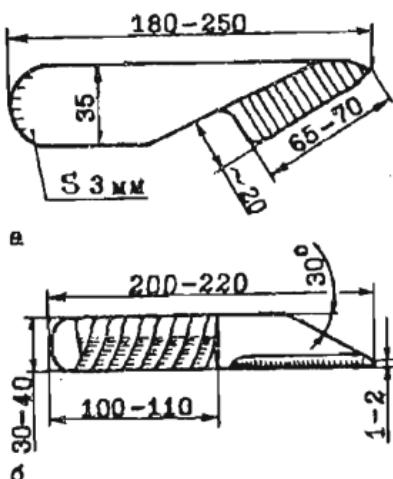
Универсальные переплетные ножи для резки картона и обрезки книжных блоков: а - с режущей пяткой; б - с режущим острием
